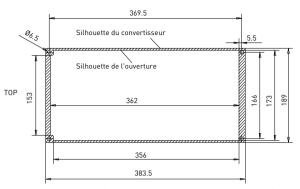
dimensions de découpe en montage par bride, pour MI4 (unité: mm)
